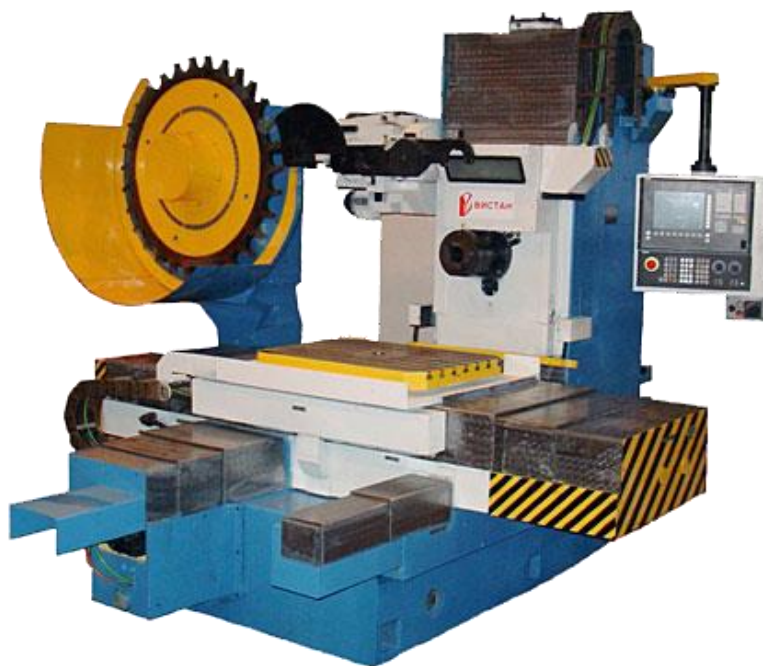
Типовий загальний вигляд багатоцільових верстатів, на яких виконують фрезерно-свердильно-розточні операції.
